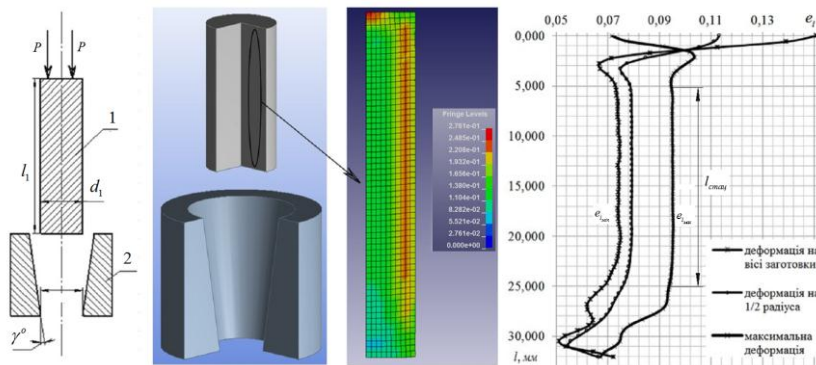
Редукування заготовки (1 – заготовка, 2-матриця)
